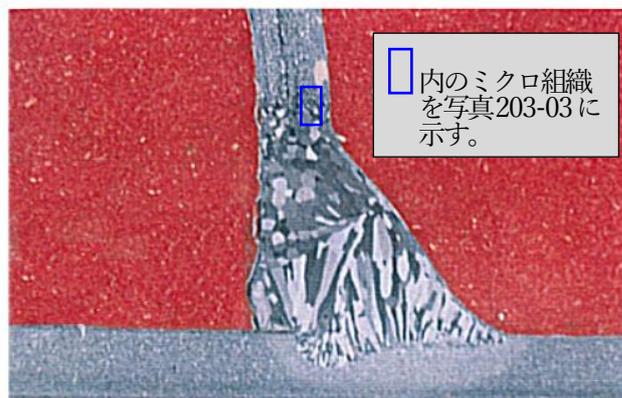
T字すみ肉溶接部のマクロ組織
